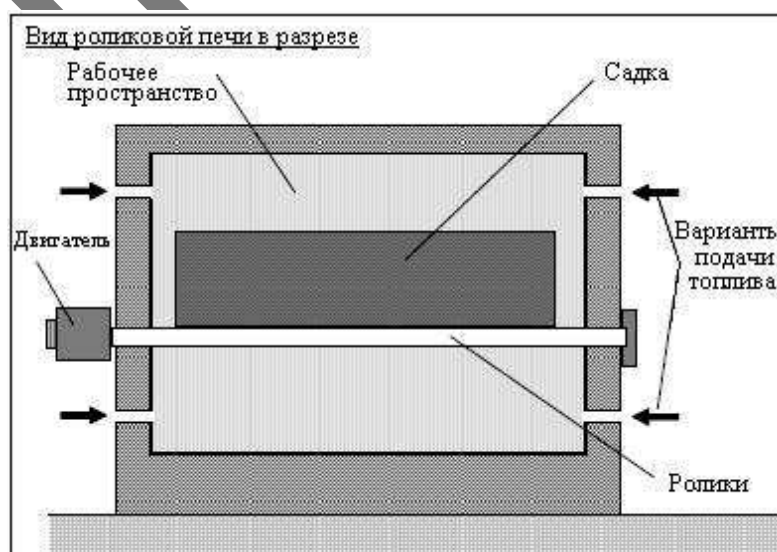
Вид роликовой печи в разрезе
